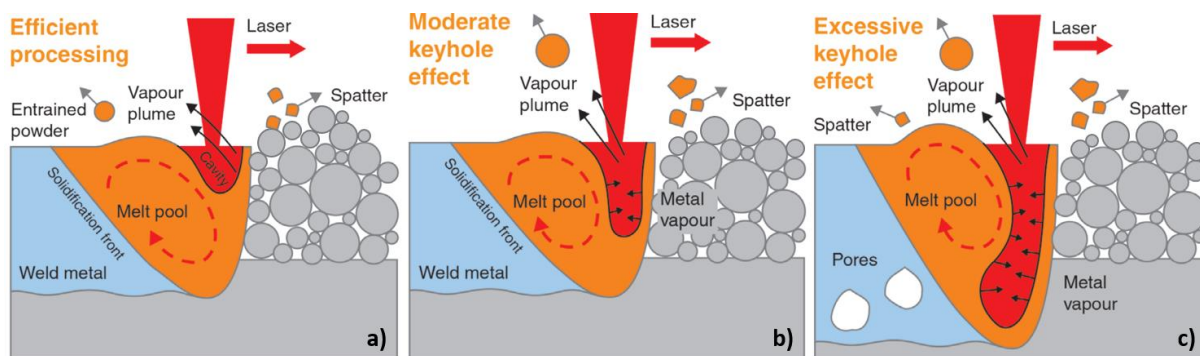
Verschiedene Schweiß-Modi (schematisch) beim L-PBF aus Saunders [52], a) Wärmeleitungsschweißen (Conduction-Mode Welding), b) moderates/stabiles Tiefschweißen (Keyhole Welding), c) exzessives/übermäßiges Tiefschweißen (Keyhole Welding) mit Prozess-Porenbildung
